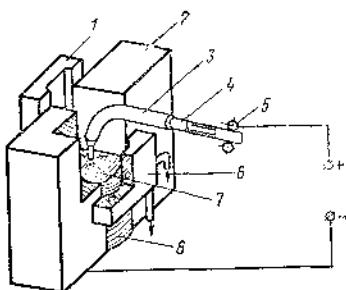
Схема сварки порошковой проволокой с принудительным формированием сварного шва
